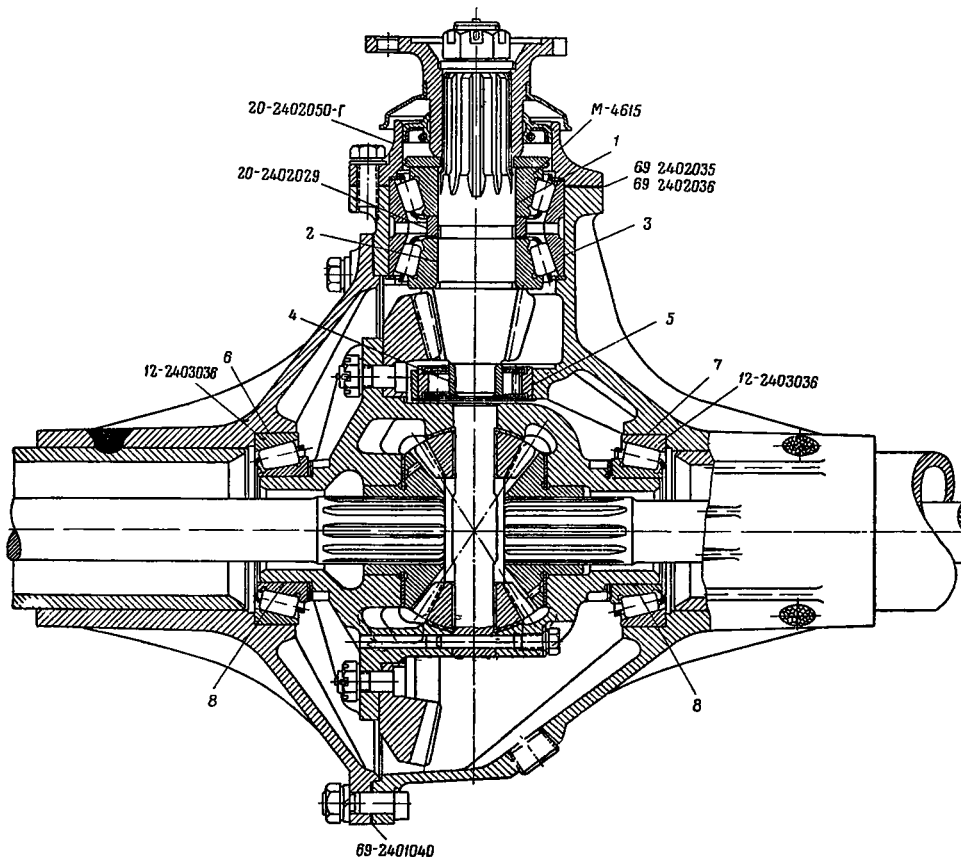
Места сопряжений при сборке картера заднего моста с крышкой картера и установке главной передачи
